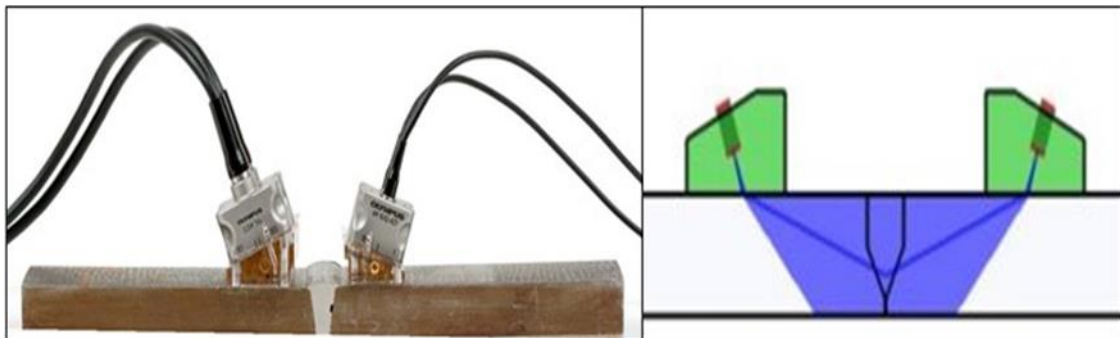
Inspección de soldadura mediante el método Phased Array.
